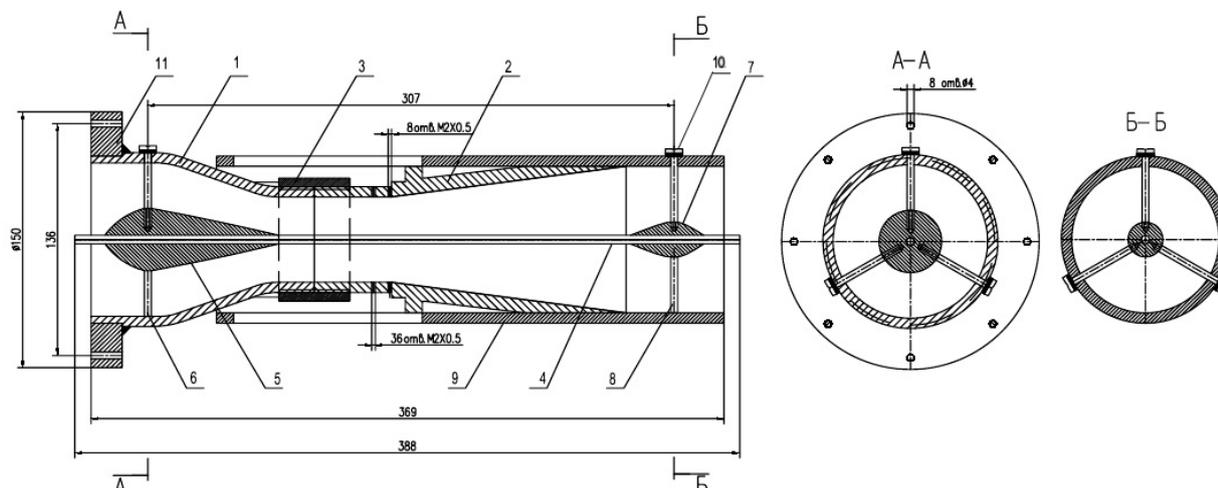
Рабочая часть установки для исследования конических диффузоров: 1 – конфузор; 2 – диффузор; 3 – резьбовая муфта; 4 – зонд; 5 – передняя опора; 6 – стержни передней опоры; 7 – задняя опора; 8 – стержни задней опоры; 9 – подвижная втулка зонда 4; 10 – ниппель; 11 – фланец
